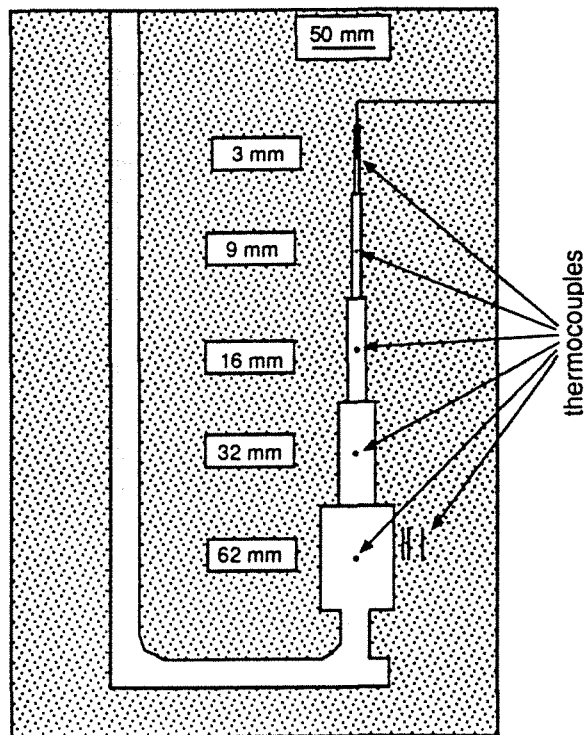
Géométrie des pièces coulées et disposition des thermocouples.
